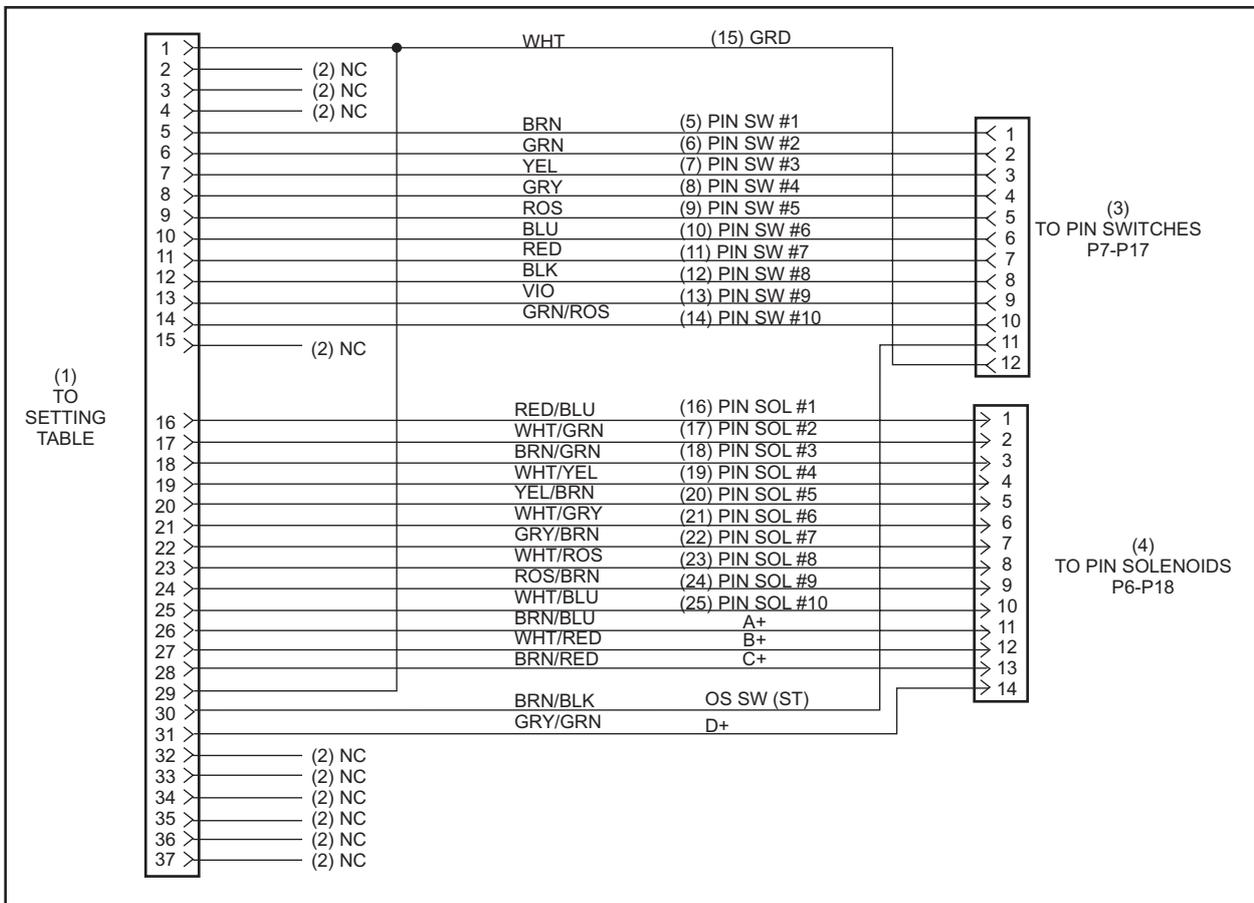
Ensemble câble plateau de positionnement externe (Pièce N° 47-245421-004)
